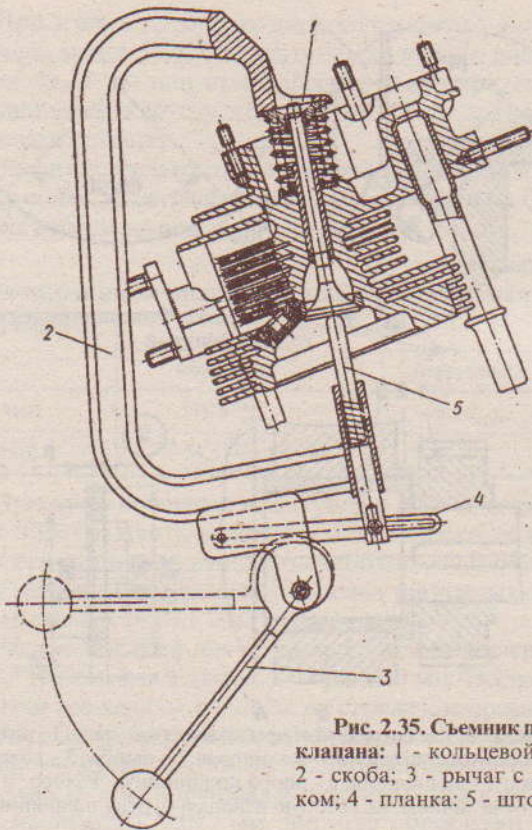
Съемник пружин клапана: 1 - кольцевой упор; 2 - скоба; 3 - рычаг с кулачком; 4 - планка; 5 - шток;
